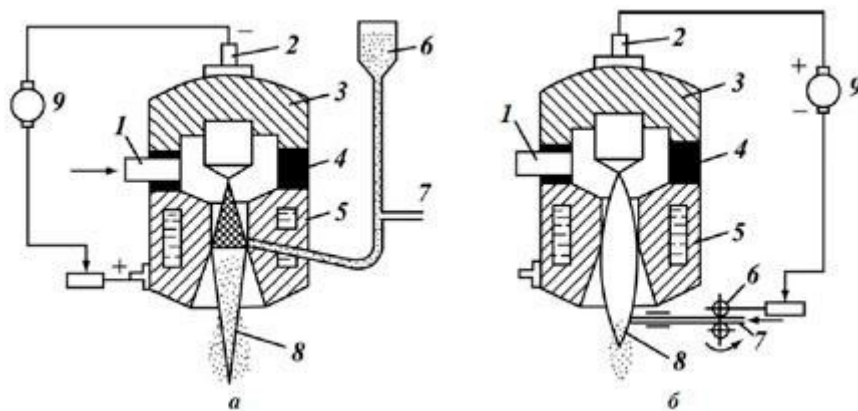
Схема плазменного напыления: а - порошком; б - проволокой. 1 - подвод плазмообразующего газа; 2 - катод плазмотрона; 3 - корпус катода; 4 - изолятор; 5 - корпус анода; 6 - порошковый питатель (рис. а) или механизм подачи проволоки (рис. б); 7 - подвод газа, транспортирующего порошок; 8 - плазменная струя; 9 - источник питания.
